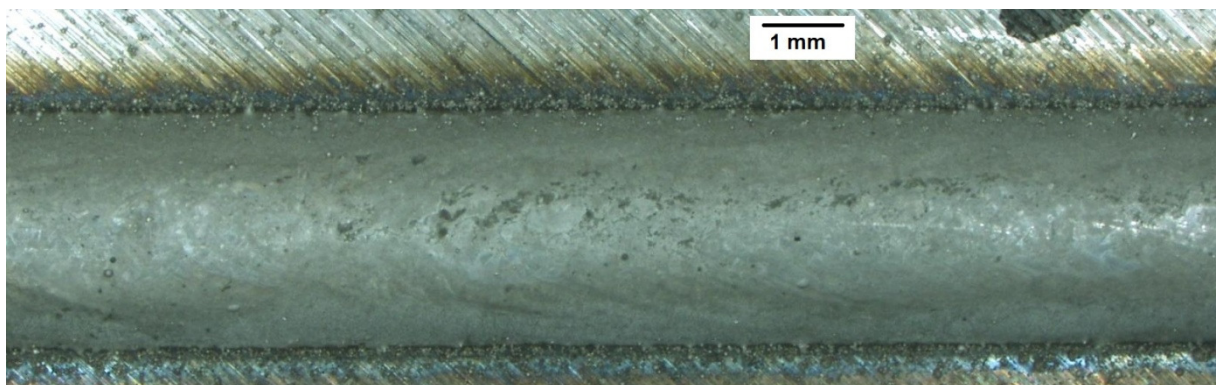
Auftragschweißspur mit einer Bearbeitungsgeschwindigkeit $v=20$ mm/s in der Draufsicht
